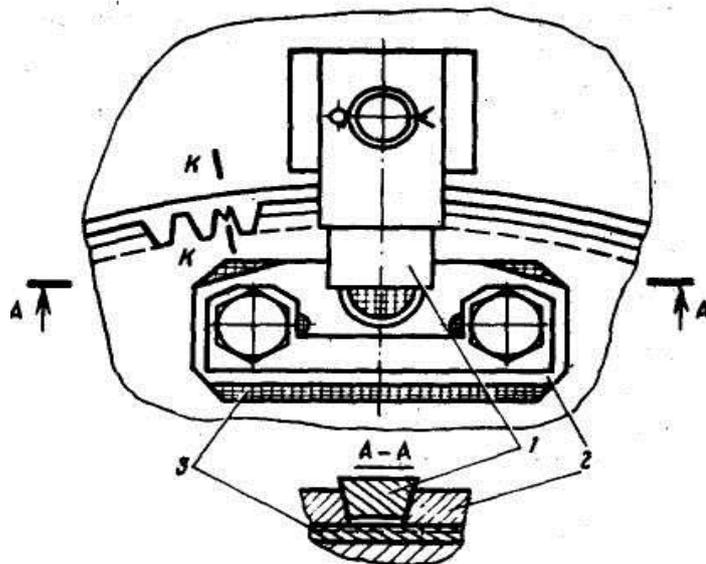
Установка траверсы тягового двигателя на нейтраль:
